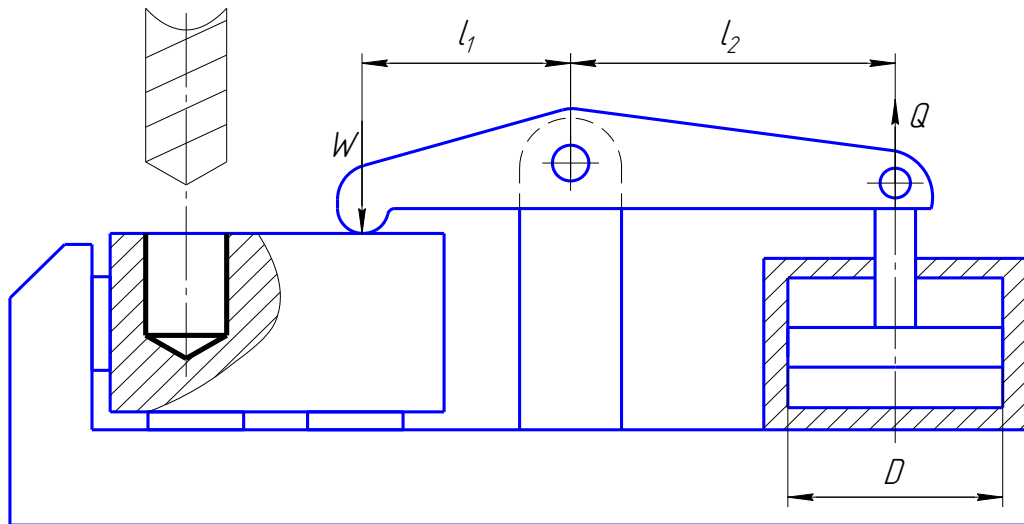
Розрахункова схема, для визначення діаметра пневмопривода затискного пристрою
